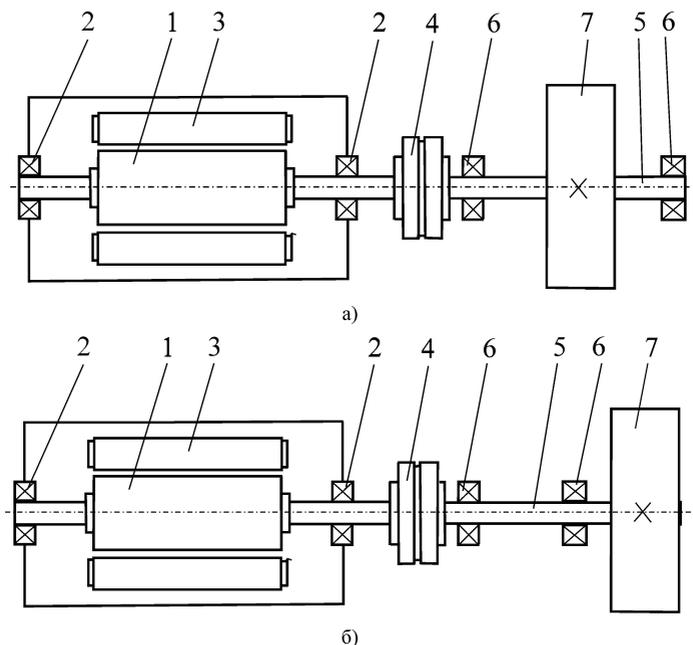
Кинематическая схема механизма: а) с межопорным; б) с консольным расположением рабочего органа
